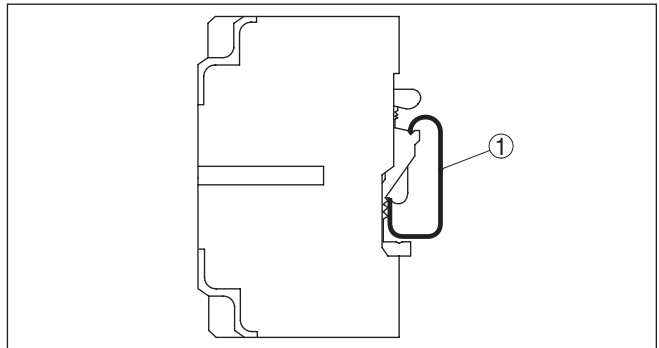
Montage sur rail porteur selon EN 50 035 (rail C) 35 x 7,5 mm
